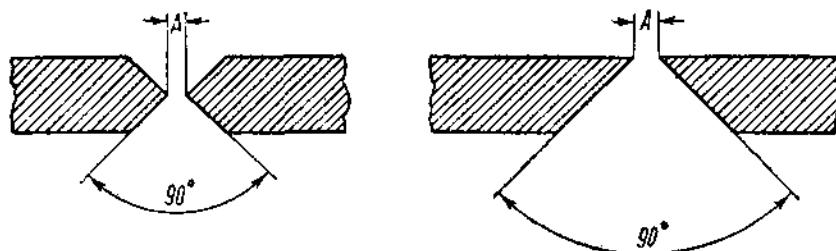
и 100. Подготовка листов к сварке.
